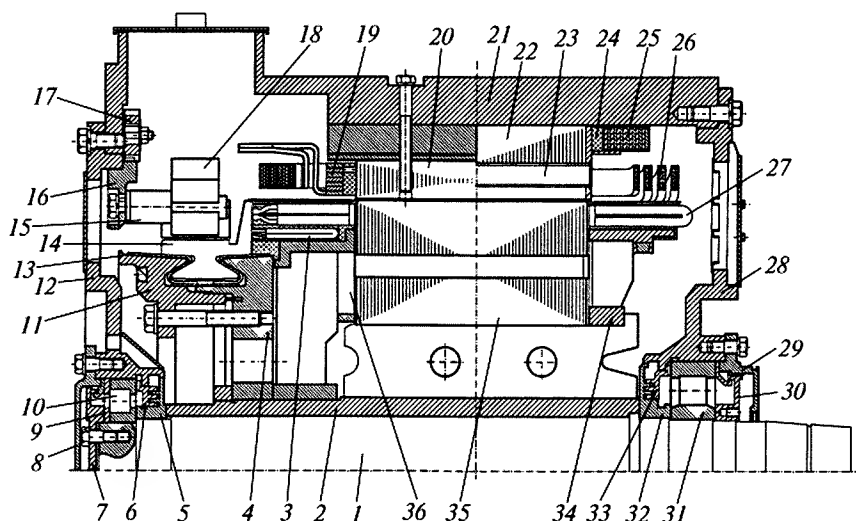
Разрез тягового электродвигателя ДТК-800КЭ:
